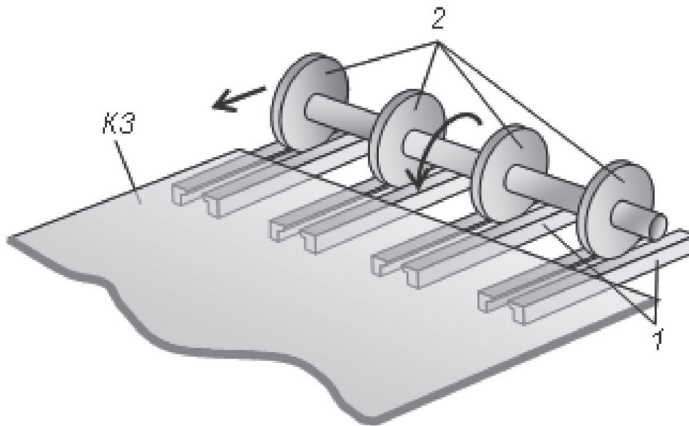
Принципова схема засобу виготовлення пазів у заготовках з гофрокартону ножичним різанням дисковими інструментами
